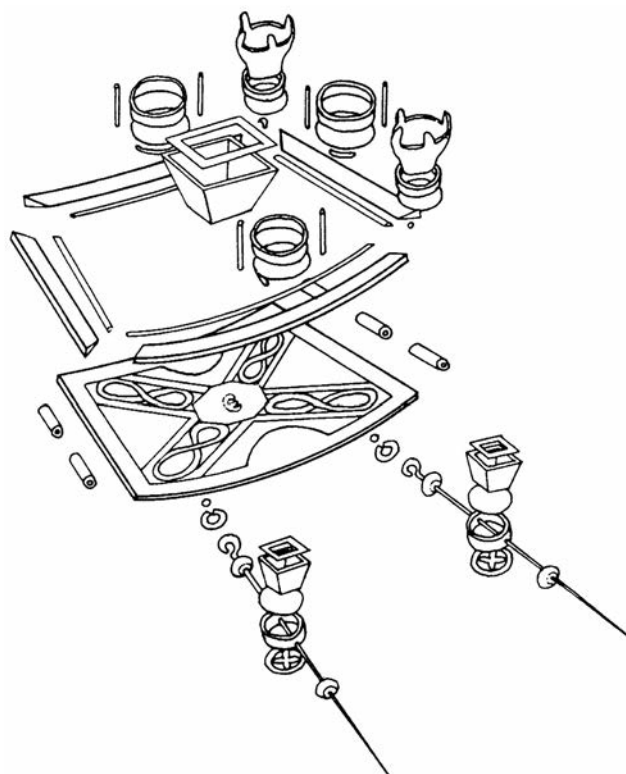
Juwelenkragen Berlin, Aufbau eines Trapezes.
